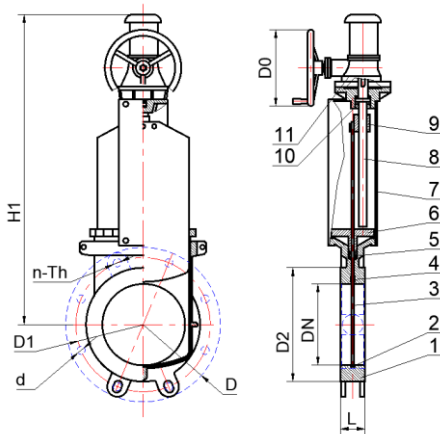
Шиберная задвижка с редуктором DN 50 – 900
